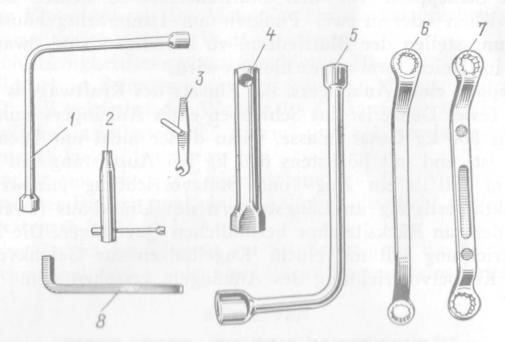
Sonderschlüssel im Werkzeugsatz des Kraftwagens:
